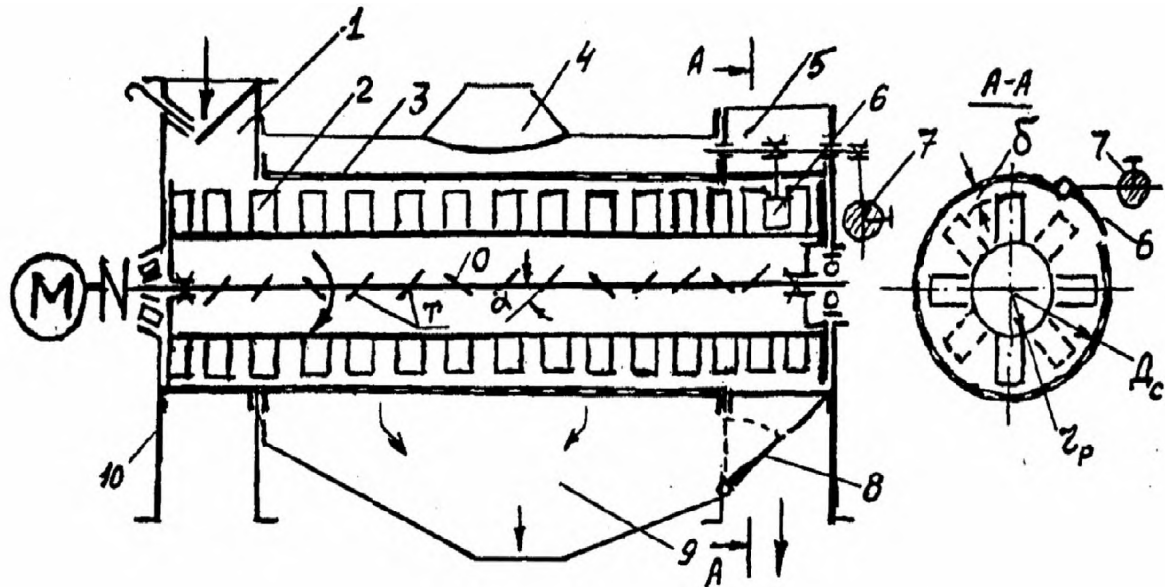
Принципова схема машини: 1 - живильник; 2 - лопатка; 3 - сито; 4 - патрубок аспірації; 5 - вихідний патрубок; 6 - клапан; 7 - противага; 8 - лапай перекидний; 9 - збірник; 10 - станина
